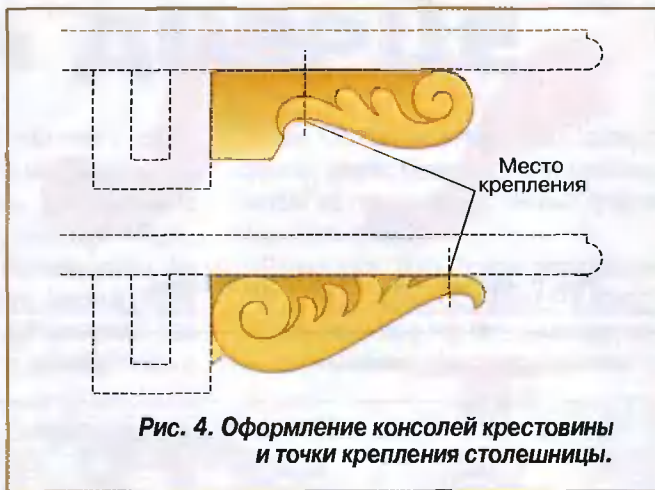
Оформление консолей крестовины и точки крепления столешницы.
